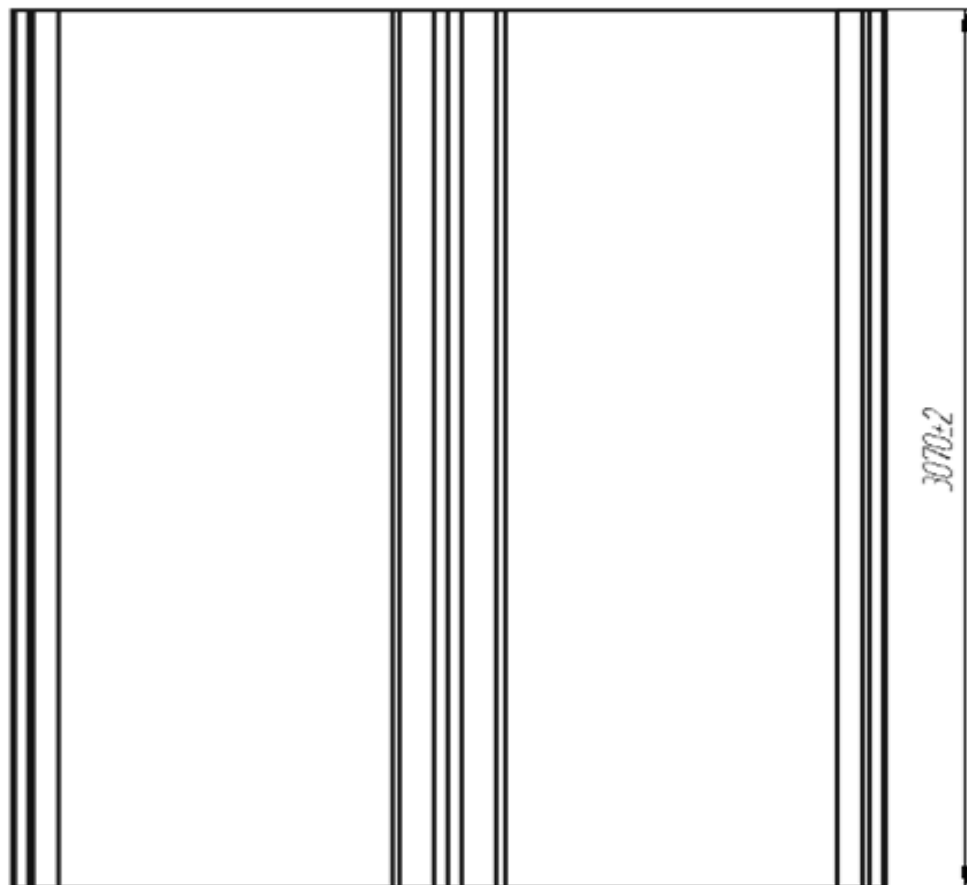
Чертеж поперечной балки (вид сверху)
